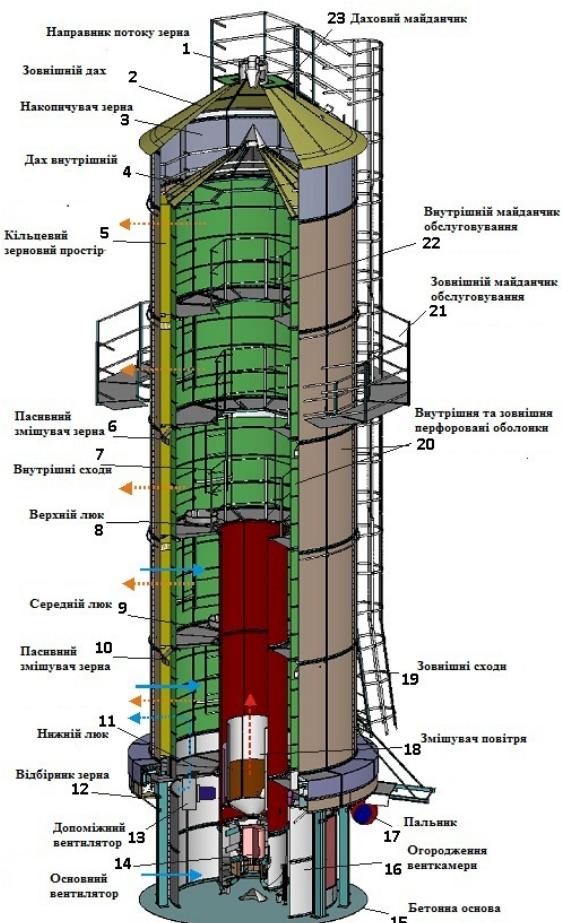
Конструкція баштової сушарки фірми "Астра"
